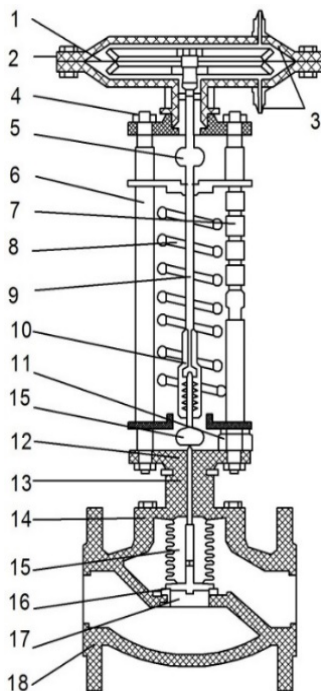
Регулятор давления JVD-JVF; 1 – мембрана; 2 – корпус мембраны; 3 – фитинги для импульсных трубок; 4 – сальниковое уплотнение; 5 – соединительный узел; 6 – крепежный стержень; 7 – стержень с калибровочными обозначениями; 8 – пружина; 9 – шток; 10 – шпindelь; 11 – регулирующая гайка; 12 – сальниковое уплотнение; 13 – тефлоновые кольца; 14 – крышка; 15 – разгружающий сильфон; 16 – тарелка клапана; 17 – седло клапана; 18 – корпус клапана
